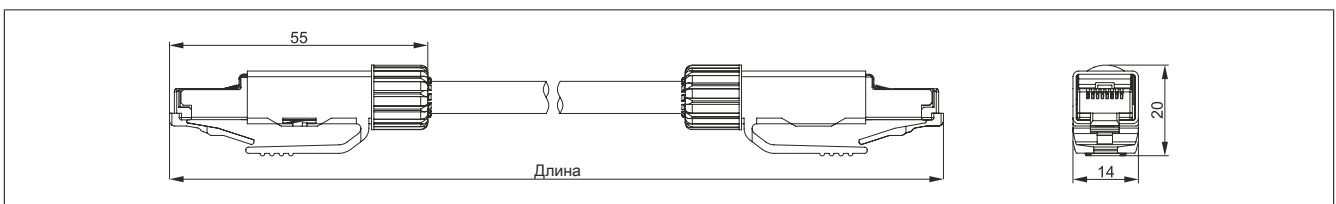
5CASD3.xxxx-00 — Размеры
